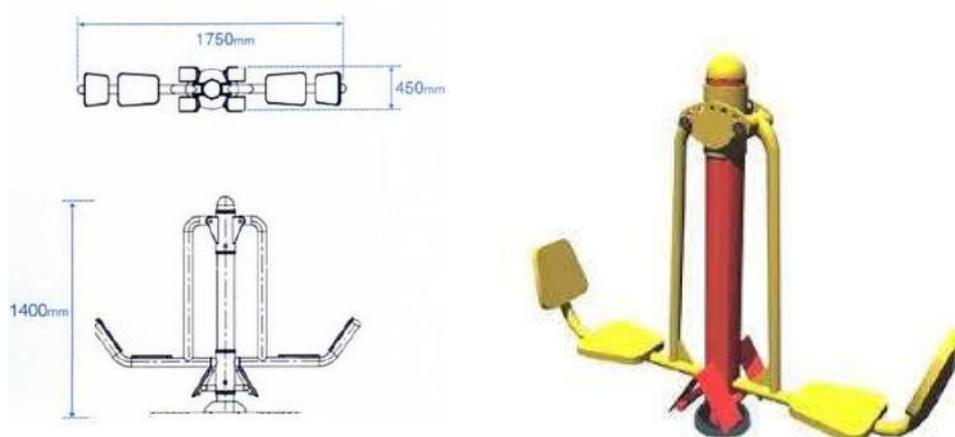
Alzado, perfil y representación 3D pectoral
